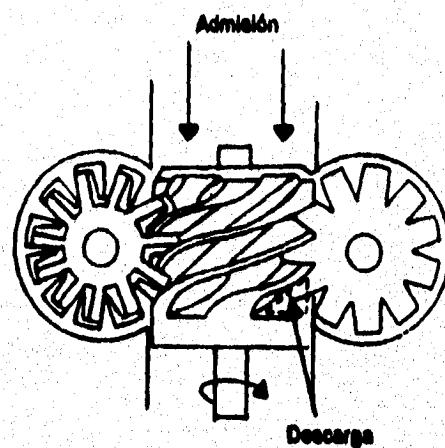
Tornillo de un compresor de tornillo único con las ruedas de estrella a cada lado.
